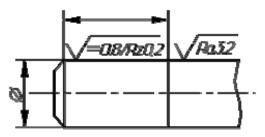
Пример обозначения различной шероховатости на одной поверхности
